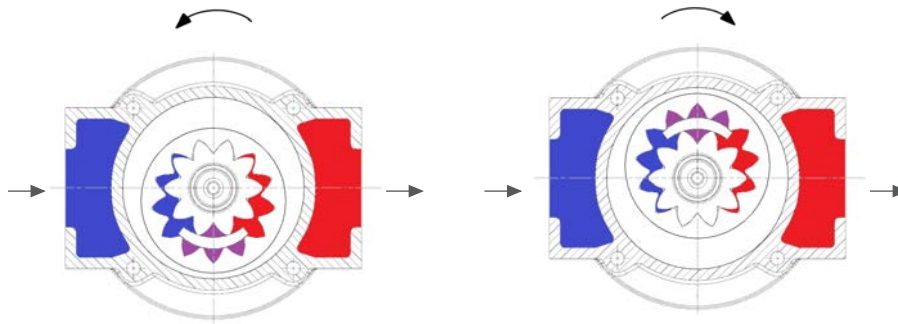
Princípio de bombeamento da bomba de engrenagens internas
